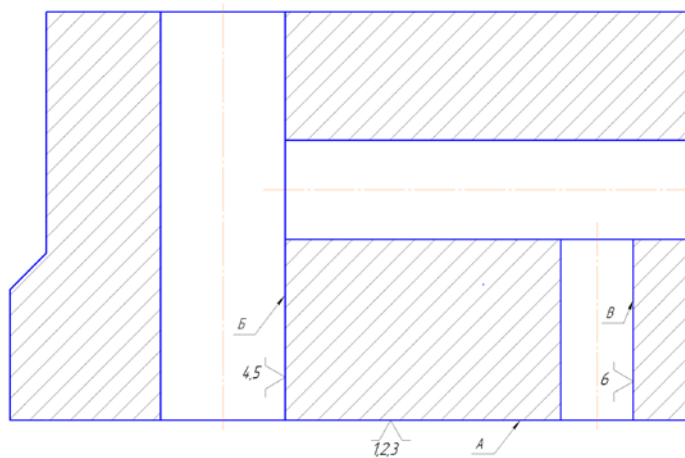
Черновые базы предлагаемого тех. процесса
